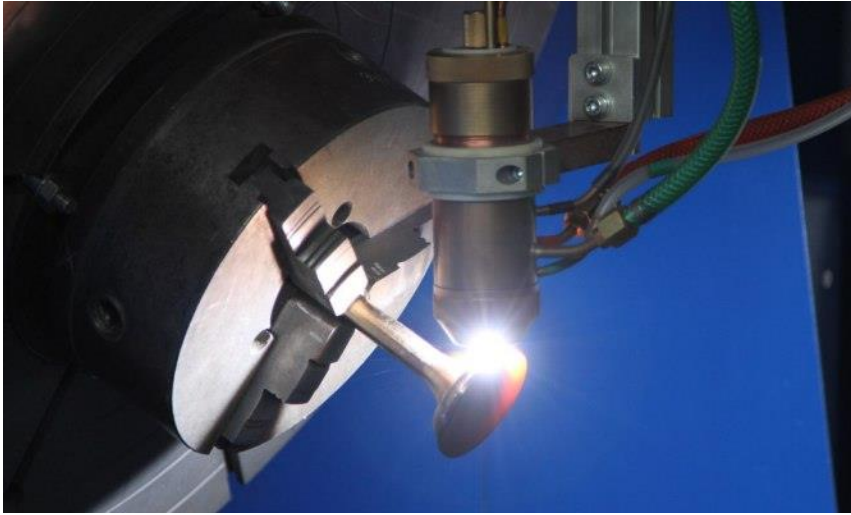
Плазмове нанесення металевго шару на поверхню деталі [4]
